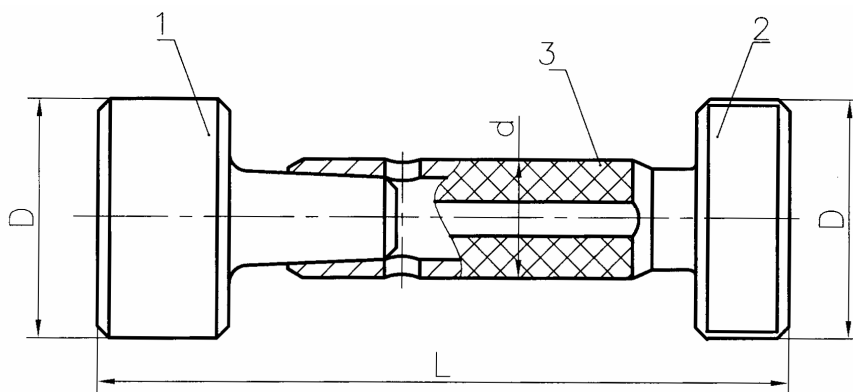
Калибр-пробка гладкий двусторонний с неполной вставкой НЕ:
